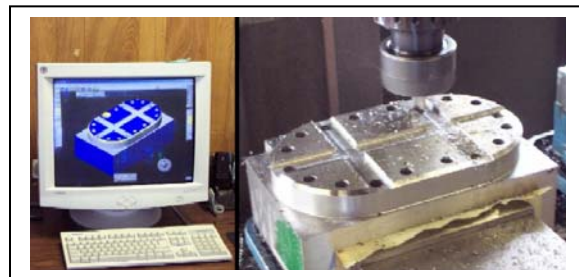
Sistema de *CAD/CAM* integrado a una máquina fresadora
